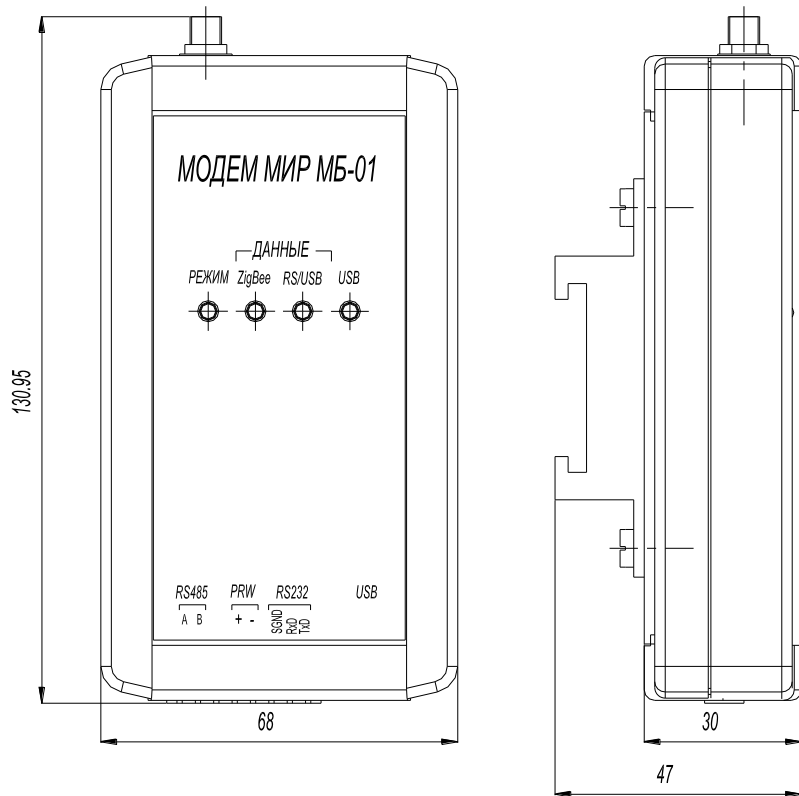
Внешний вид и габаритные размеры модема МБ-01.ВД
